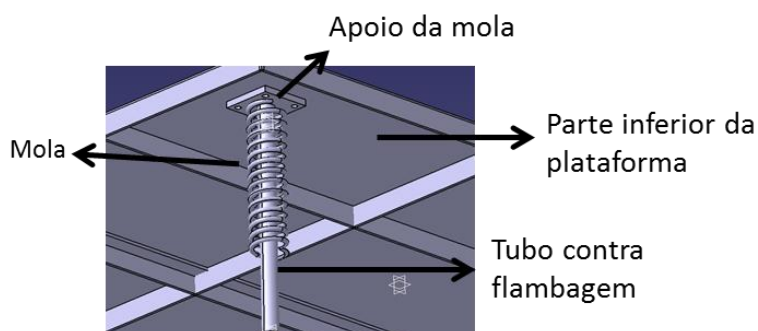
Desenho CAD do tubo guia para o trabalho da mola.
